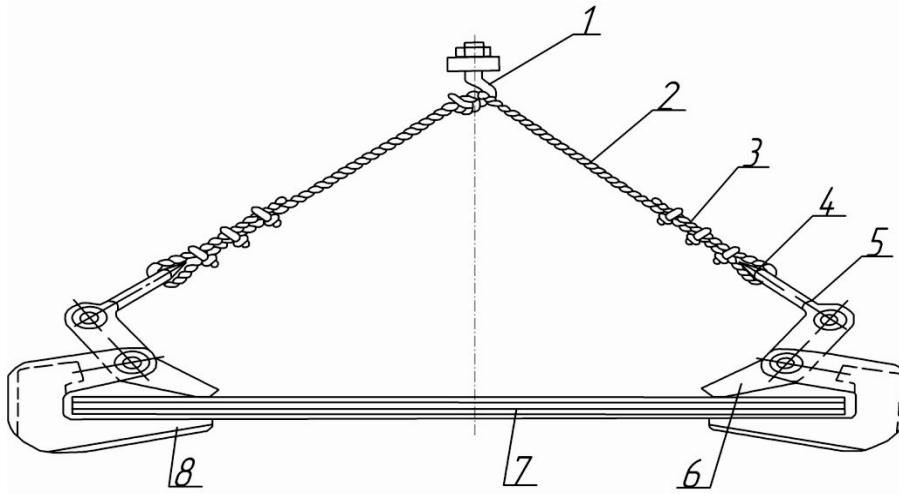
Захоплювач для підймання пакета листів металу:
